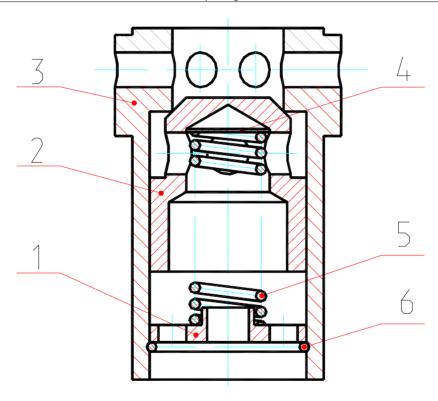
Клапан предохранительный Fig. 22 Safety Valve
